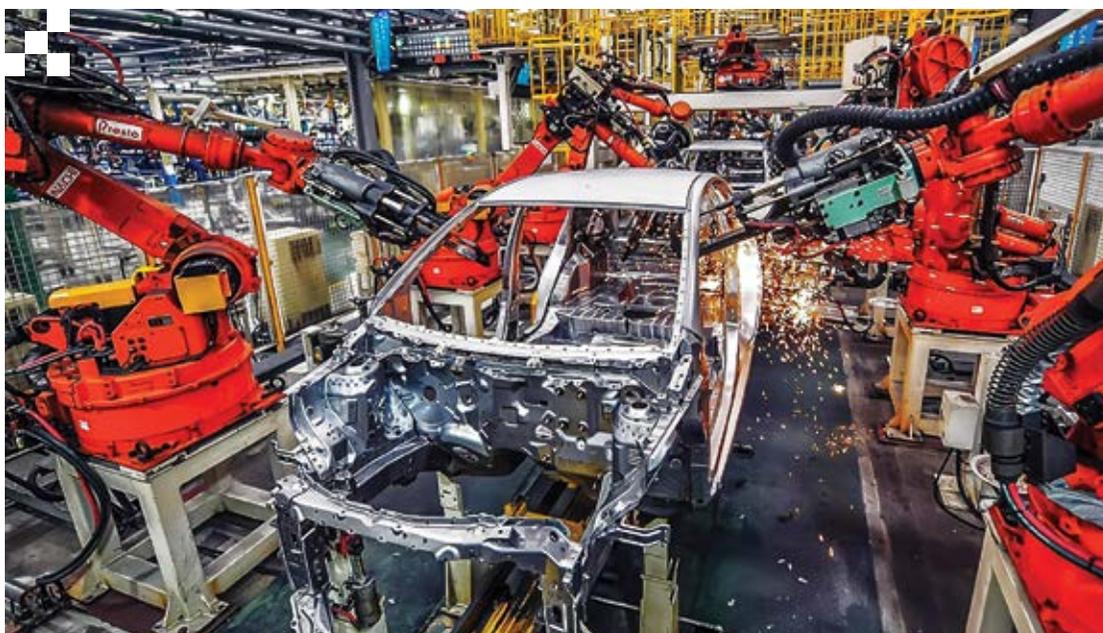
Estación de soldadura mediante brazos de robot en una planta automotriz.
